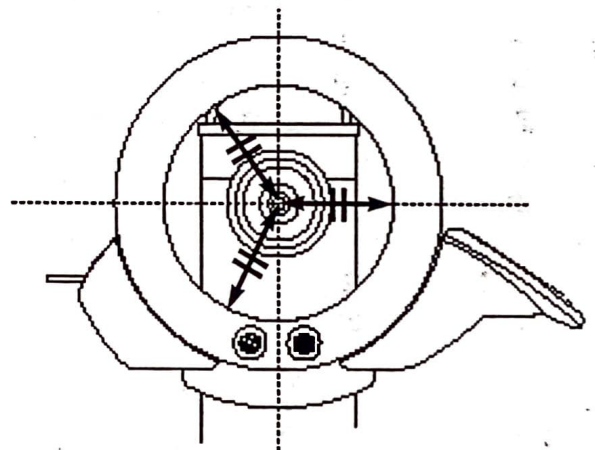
Le pilote doit être centré sur l'axe de barre
